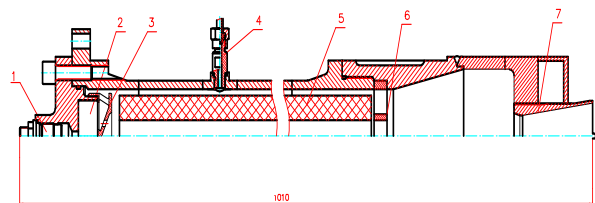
Конструктивная схема опытного РДТТ: 1 – пиропатрон; 2 – воспламенитель; 3 – рассекающий; 4 – штуцер замера давления; 5 – заряд твердого топлива; 6 – диафрагма; 7 – сопловой блок
